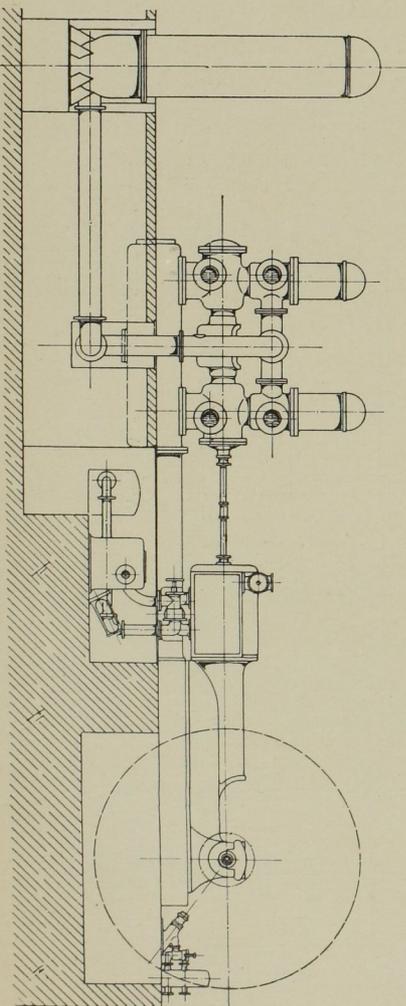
Wasserwerk Tübingen. Pumpmaschine. Massst. 1:120.
